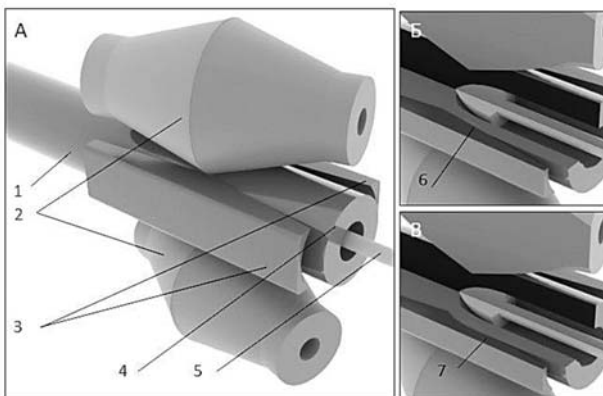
Очаг формоизменения (деформации): а — схема винтовой прошивки; б, в — ступенчатый разрез очага формоизменения с демонстрацией выходного участка линейки; 1 — заготовка; 2 — бочковидные валки; 3 — направляющий инструмент (линейки); 4 — гильза; 5 — оправка; 6 — профиль выходного участка линейки; 7 — выходной участок линейки с криволинейной вогнутостью
